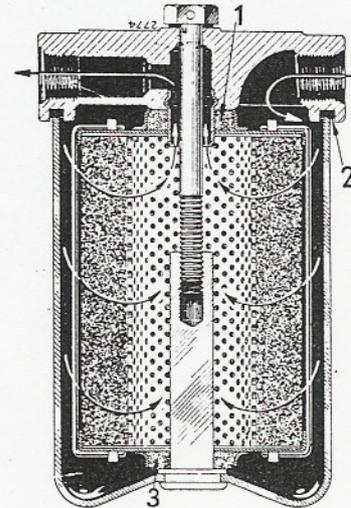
Filtre à carburant Bosch FJ/DF 5303
